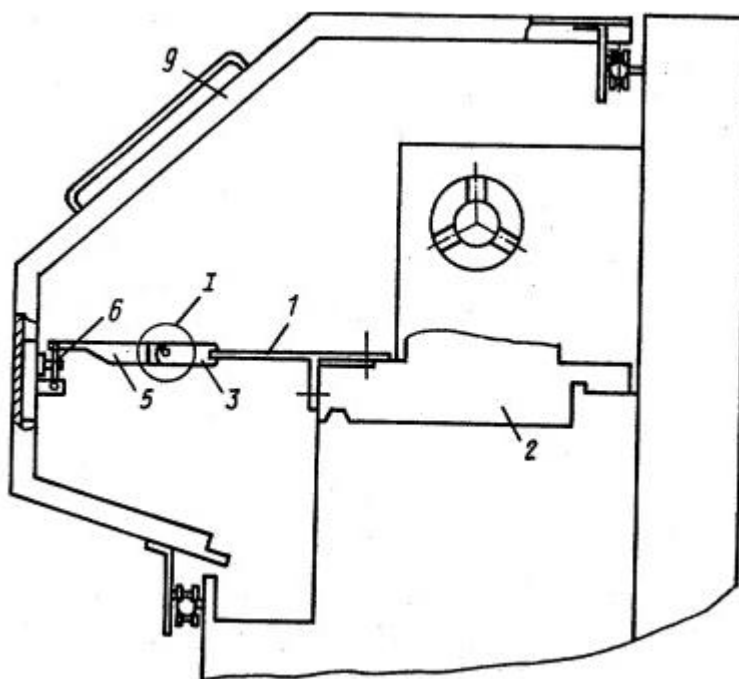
Устройство для ограждения зоны резания токарного станка
